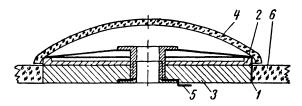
Крепление конденсатора КПК-2. 1—слой клея БФ-2; 2— подвижная часть конденсатора; 3 неподвижная часть конденсатора; 4— ручка настройки; 5 контактный вывод; 6— корпус приемника.
